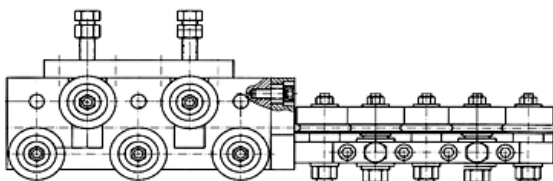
Схема конструкции двухплоскостного устройства для знакопеременного изгиба калиброванного проката / Fig. 1. Scheme of the construction of a two-plane device for alternating bending of calibrated rolled steel
